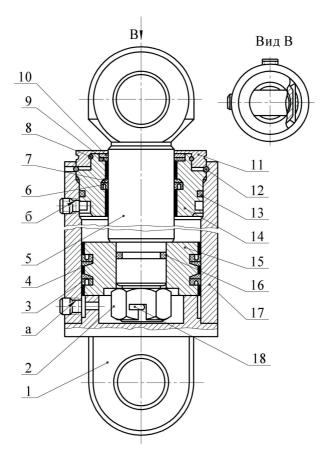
Гидроцилиндр: 1 – проушина; 2 – гайка; 3 – манжета; 4 – защитное кольцо; 5 – шток; 6 – манжета; 7 – защитное кольцо; 8 – стопор; 9 – грязесъемник; 10 – кольцо; 11 – втулка; 12 и 13 – кольцо; 14 – крышка; 15 – поршень; 16 – кольцо; 17 – цилиндр; 18 – шплинт
